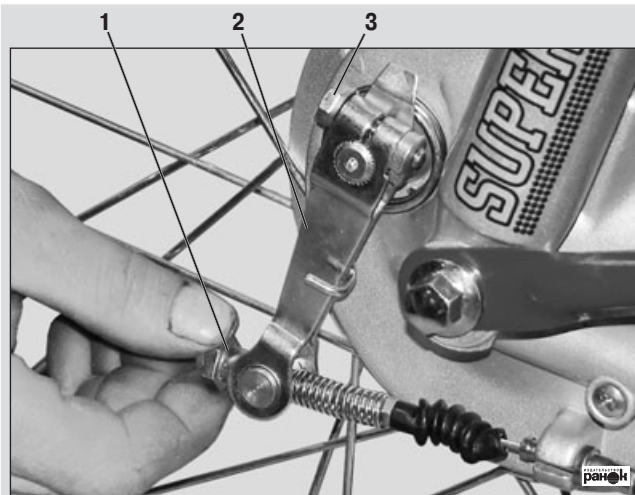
Регулировка переднего тормоза: 1 — регулировочная гайка; 2 — тормозной рычаг; 3 — гайка тормозного рычага переднего колеса
